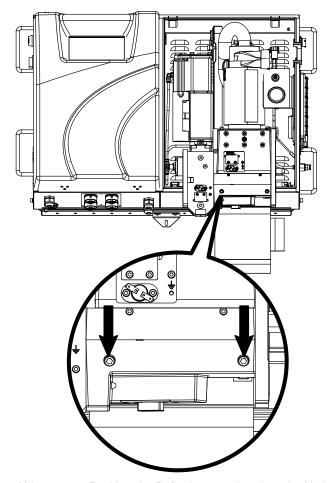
Position der Befestigungsschrauben der Hydraulikbaugruppe
